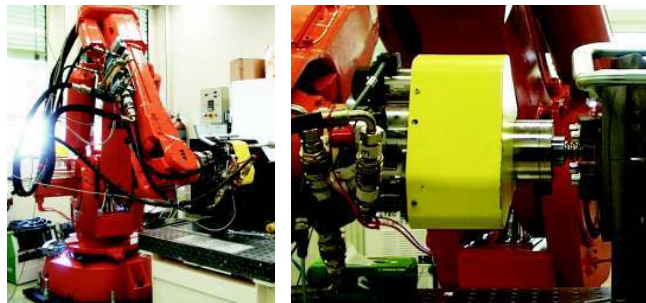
6-Achsen-Knickarmroboter(links)undSchweißkopf(rechts)
